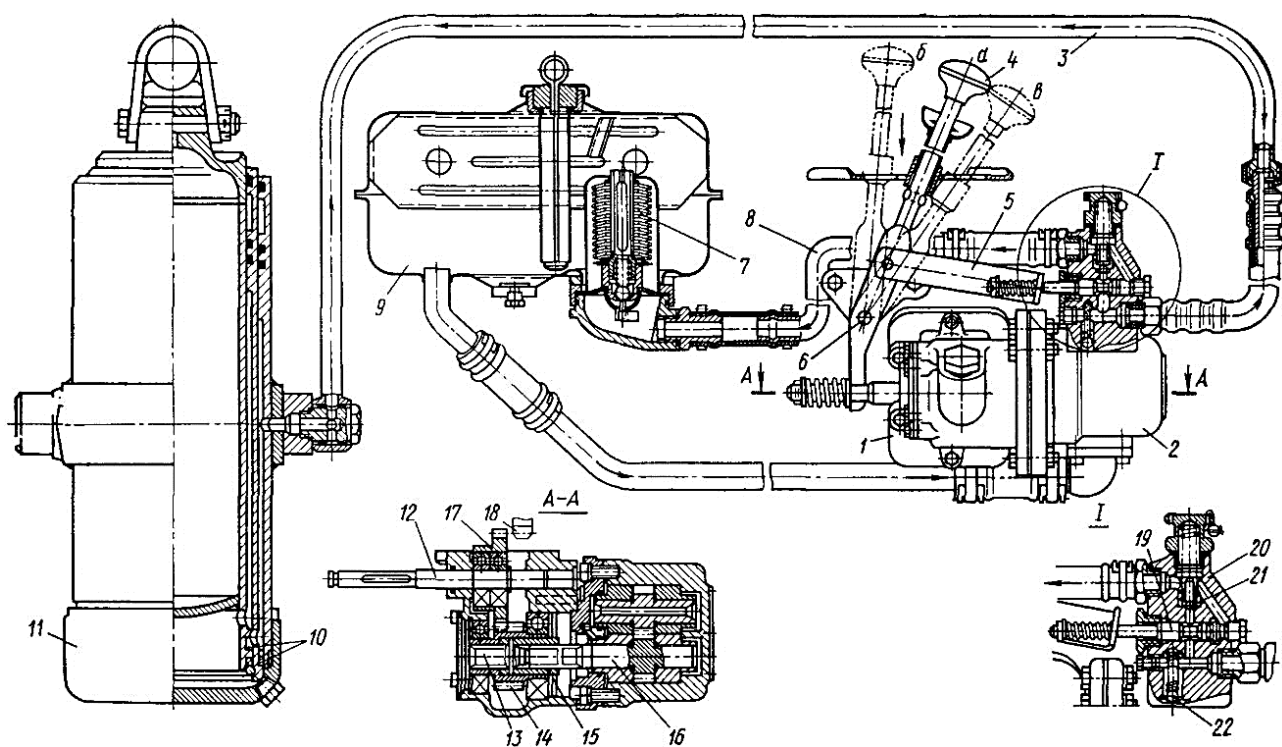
Гидропривод самосвала ЗИЛ-ММЗ-555: 1 – картер; 2 – масляный насос; 3, 8 – трубопровод; 4 – рычаг; 5 – скоба; 6, 12 – ось; 7 – масляный фильтр; 9 – масляный бак; 10 – звенья гидроцилиндра; 11 – гидроцилиндр; 13 – шлицевой валик; 14 – колесо коробки отбора мощности; 15 – втулка шлицевая; 17 – зубчатое колесо; 18 – колесо блока зубчатых колес; 19 – золотник; 20 – кран управления; 21 – шарик; 22 – обратный клапан
